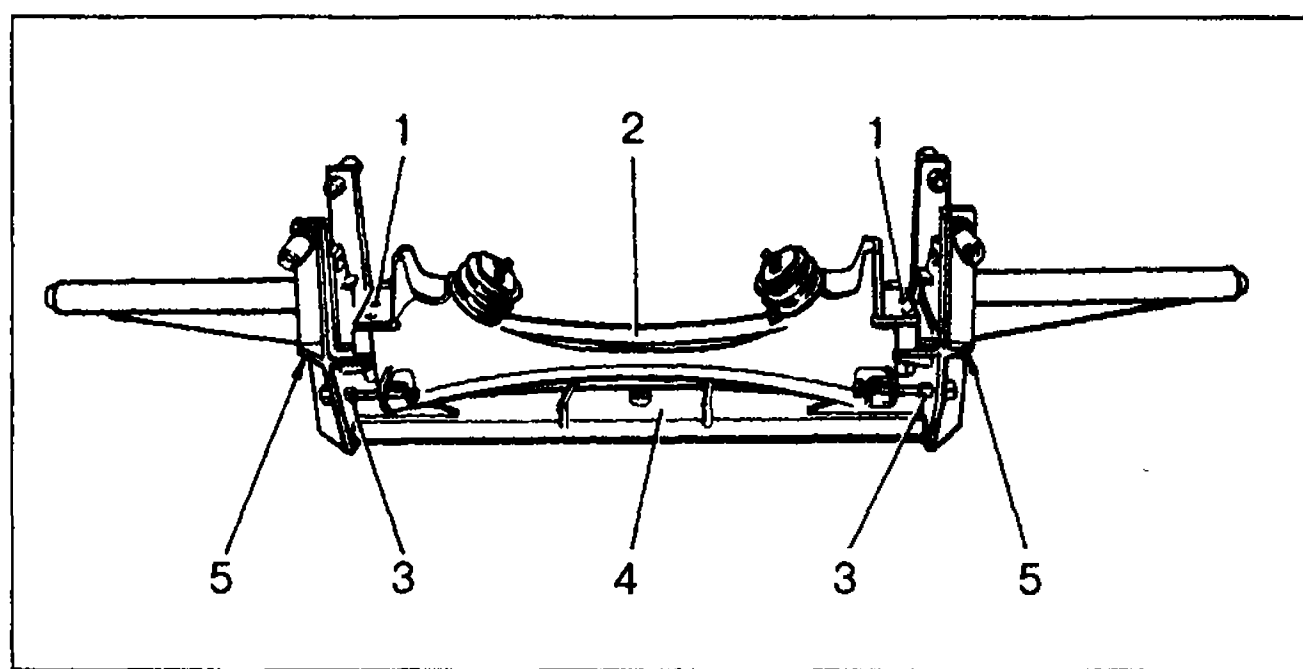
Проверка поперечины передней подвески: 1-отверстия на поперечине под установочные штыри приспособления; 2-поперечина; 3-контрольные втулки приспособления; 4-приспособление А.78124/R; 5-контрольные отверстия установки болтов на поперечине
